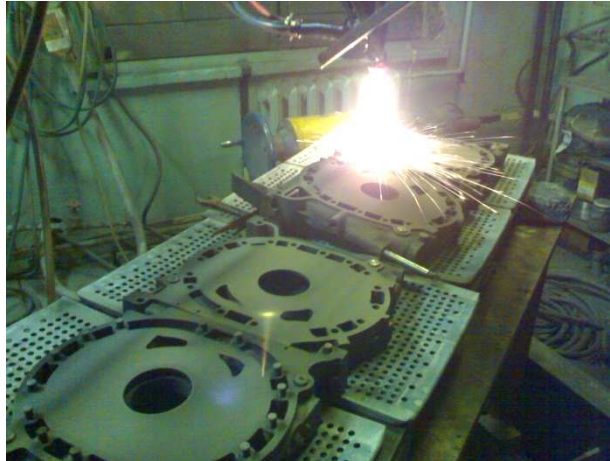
Восстановление рабочей поверхности корпусных деталей (крышек) роторно-поршневых двигателей «Mazda»
